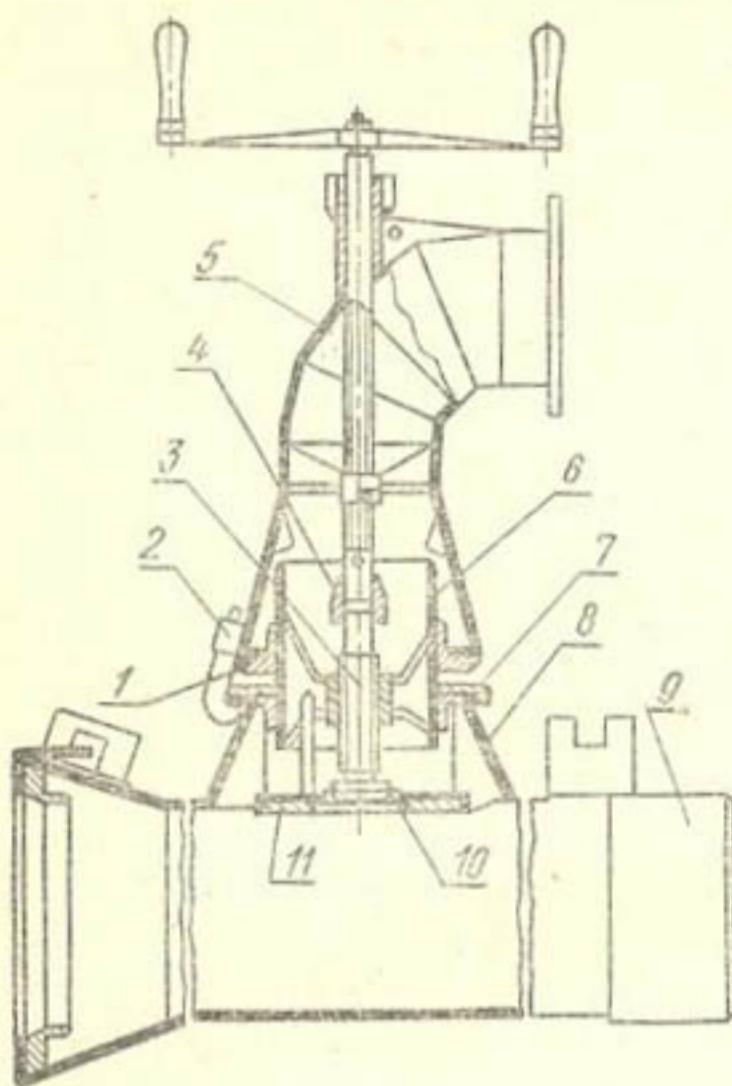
Гидрант-водовыпуск Г-180/125 для разборных трубопроводов:
